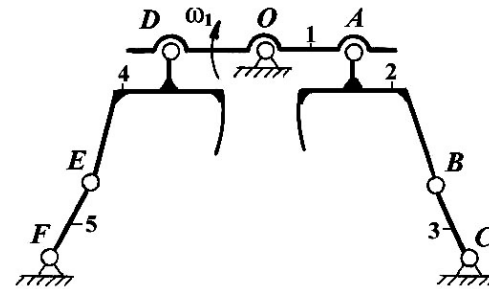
Механизм подпрессовки соломы в копнителе комбайна Дон-1500
